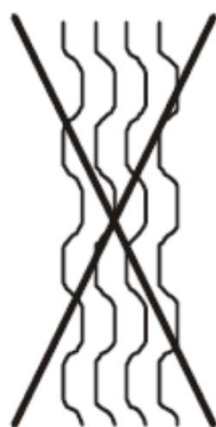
Вид пакета пластин при неправильной сборке
